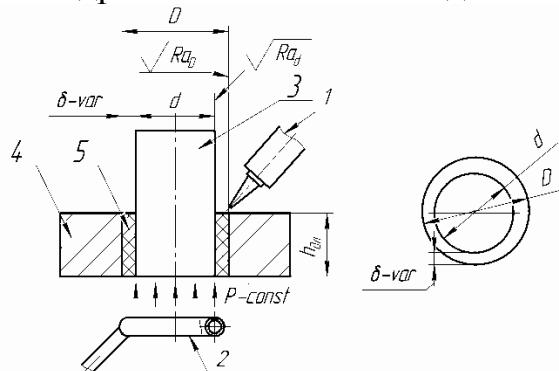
Принципиальная модель сборки регулируемых цилиндрических kleевых соединений: 1- дозатор, 2- насадка, 3- вал, 4- втулка, 5- kleевая композиция, δ - величина зазора, d - диаметр вала, D - диаметр втулки, Ra_d - шероховатость наружной поверхности вала, Ra_D - шероховатость внутренней поверхности втулки, h_{dl} - длина сопряжения, P - величина давления воздушной среды
